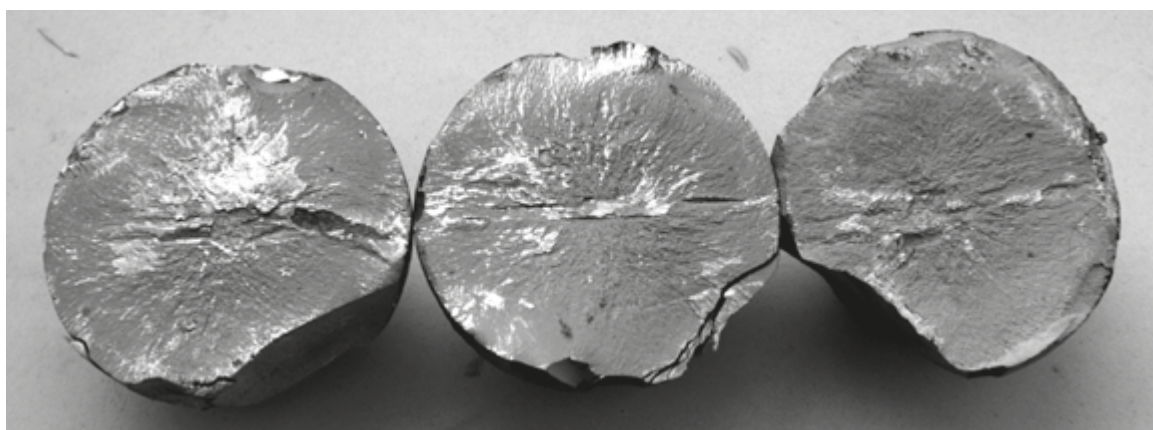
Общий вид изломов шаров, прокатанных из заготовок с флокенами
